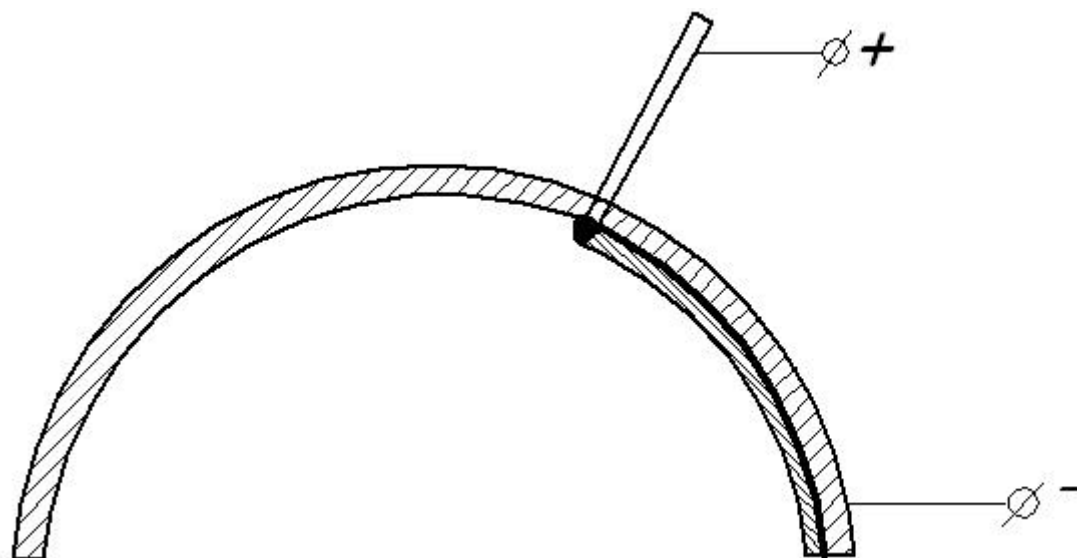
Схема ручной дуговой сварки
